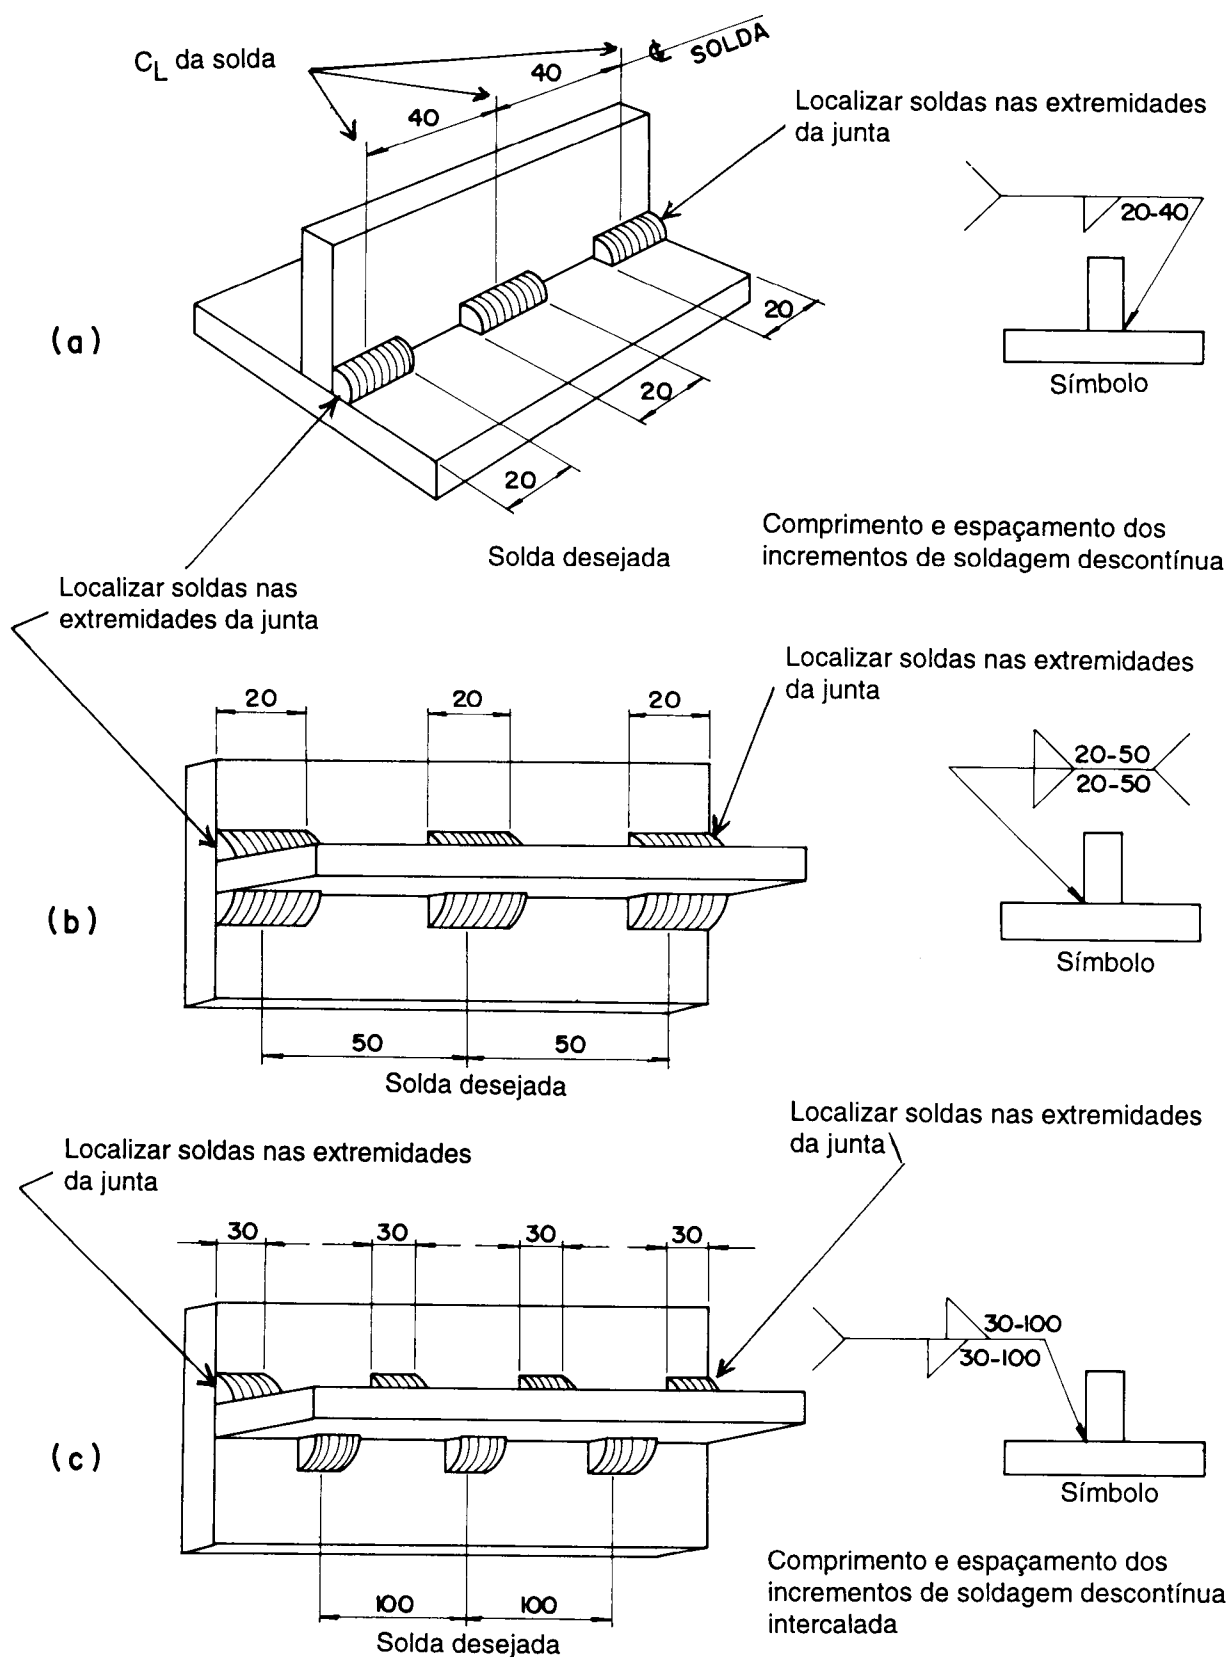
Exemplos de símbolos de soldagem descontínua
